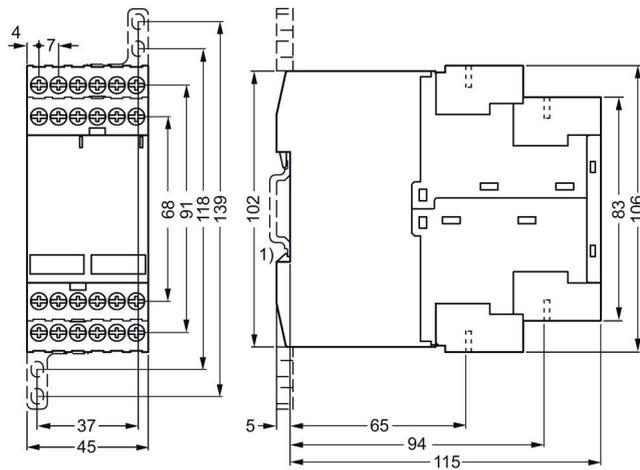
3TK2810/25/26/27/28/34/45 Schraubanschluss
